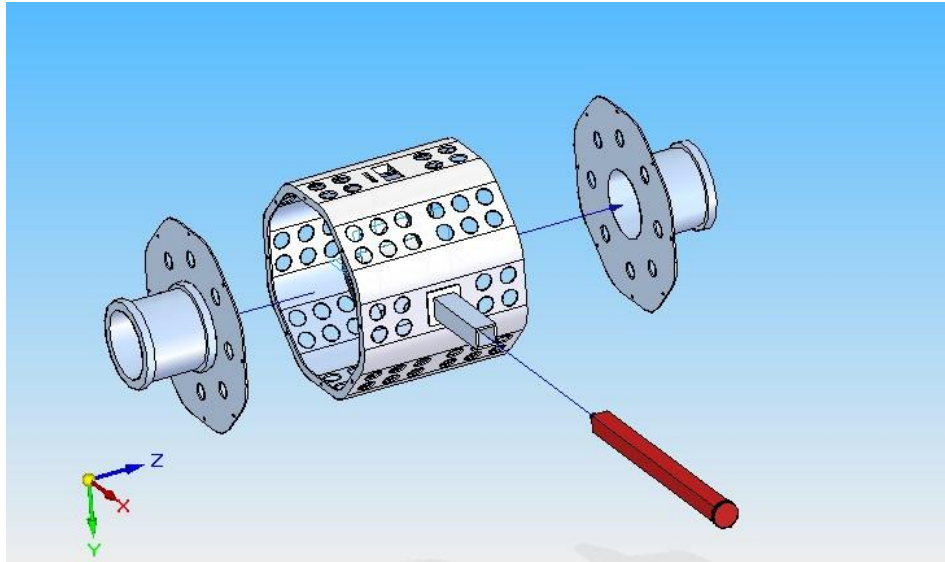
Imagen del explosionado de la carcasa, sus tapas y el brazo de par
